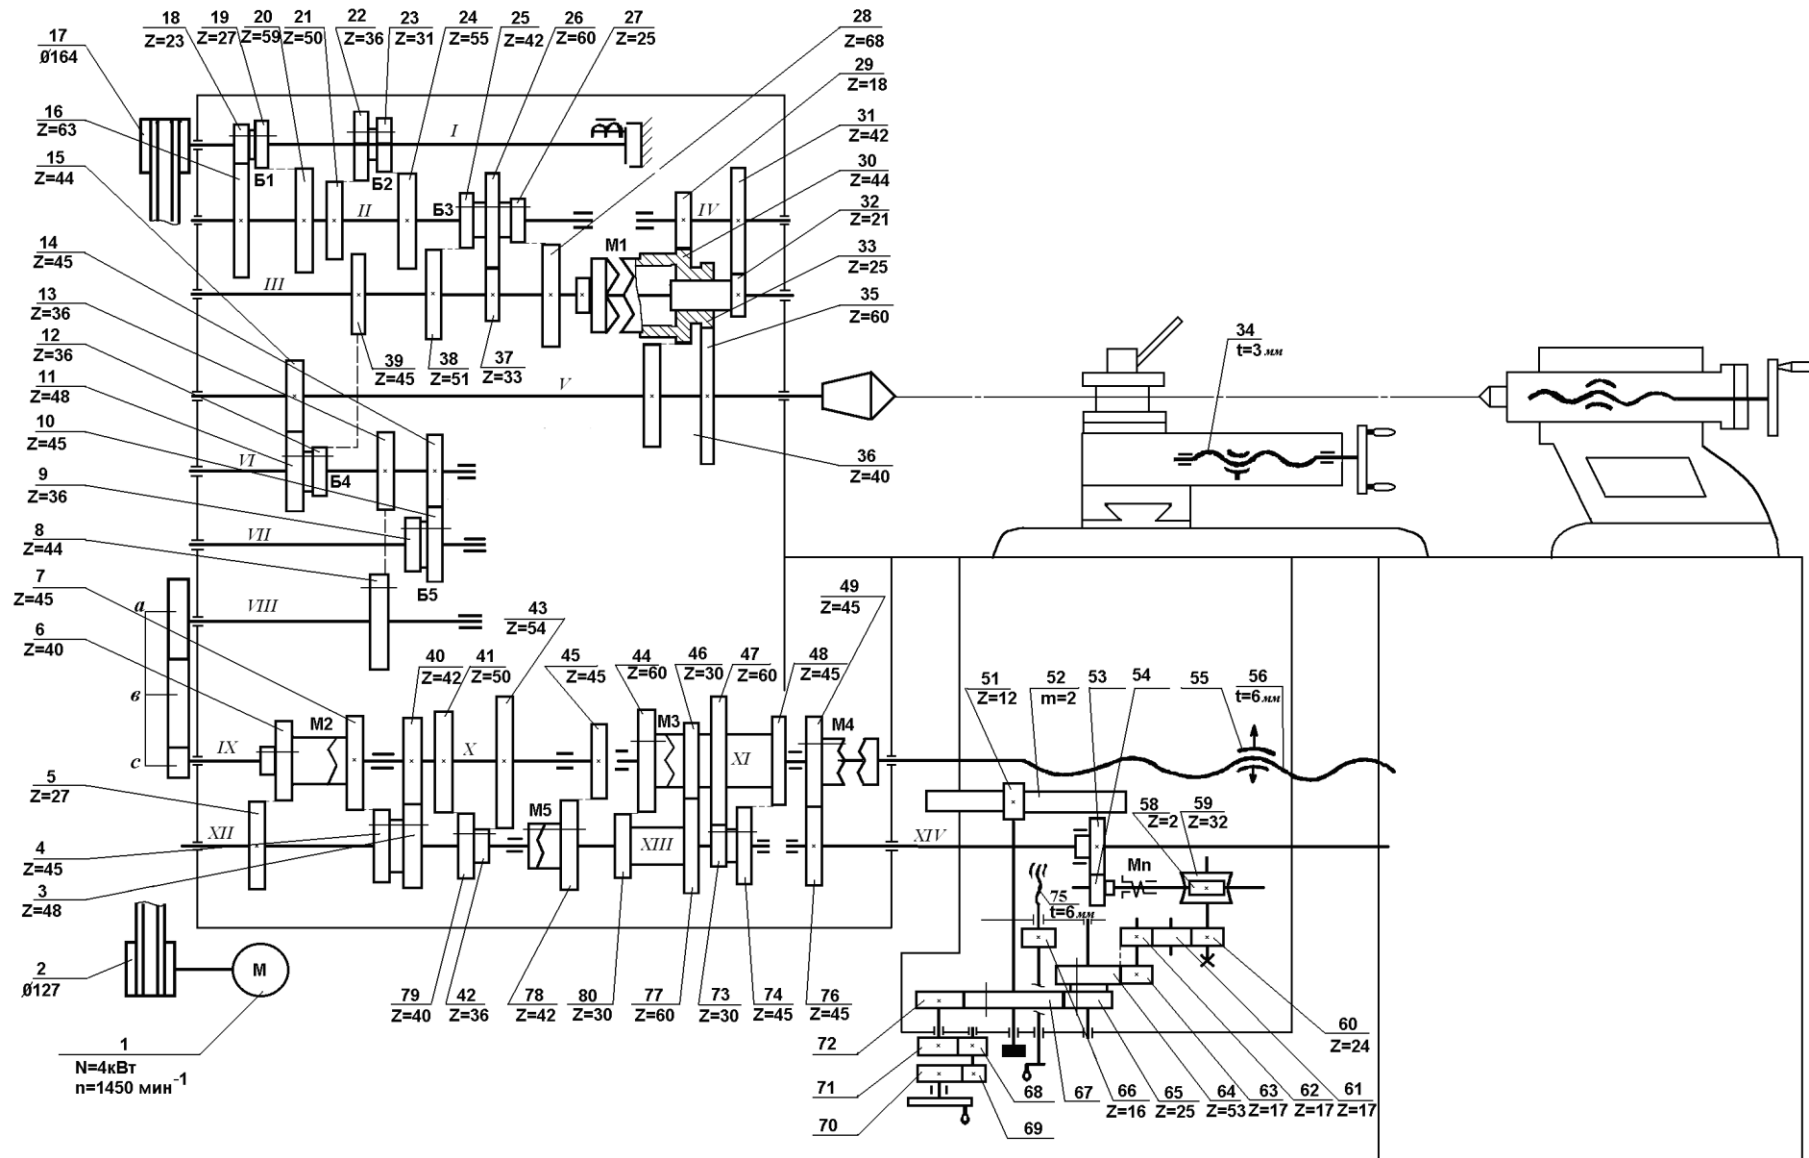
3. Кинематическая схема токарно-винторезного станка 1М61
